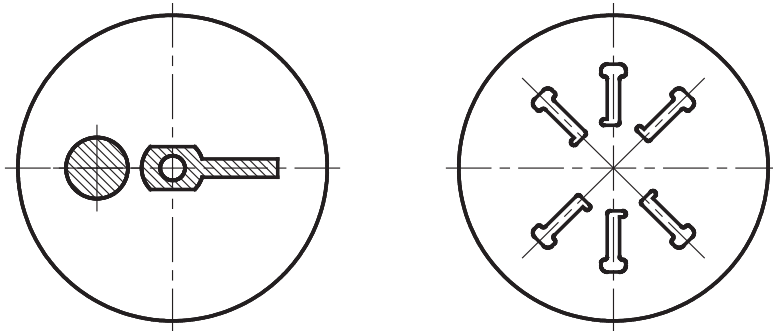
Матрицы для прессования профилей несимметричного сечения:
